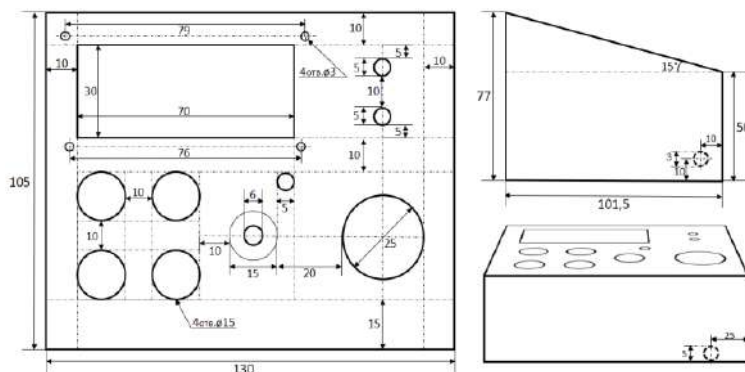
Чертёж корпуса разрабатываемого прибора
